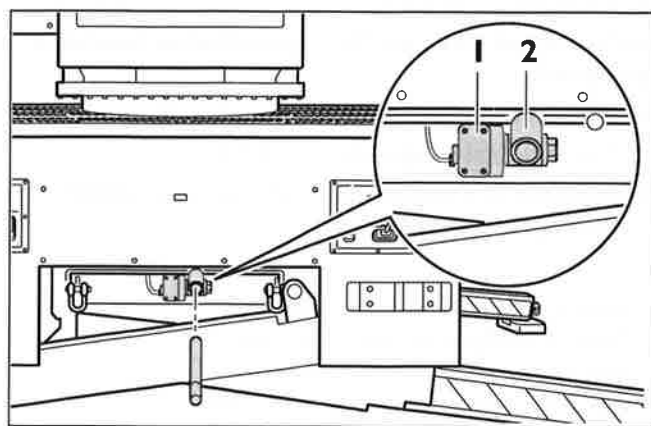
/2 Handpumpe (Pos. 1) mit Aufnahme für den Pumpenhebel (Pos. 2).
